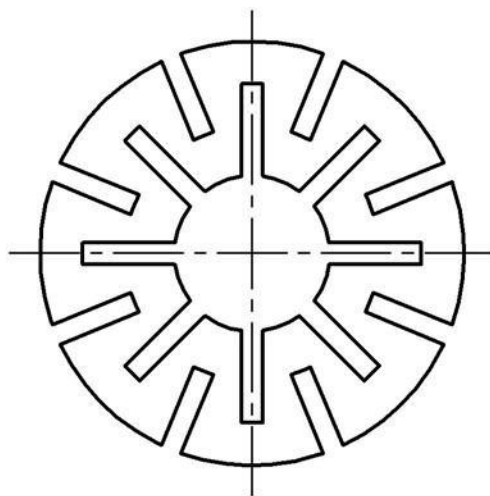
Образец чертежа Пластинчатой пружины
